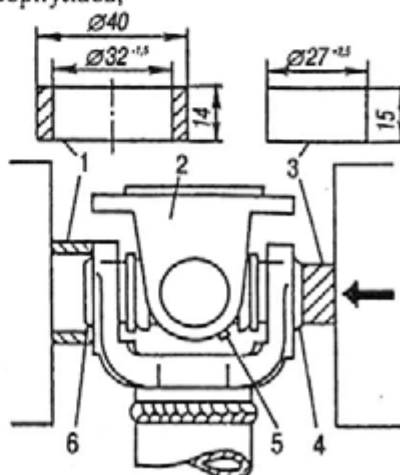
Разборка карданного шарнира: 1 - кольцо; 2 - фланец карданного вала; 3 - Оправка; 4, 6 - подшипники; 5 - масленка
